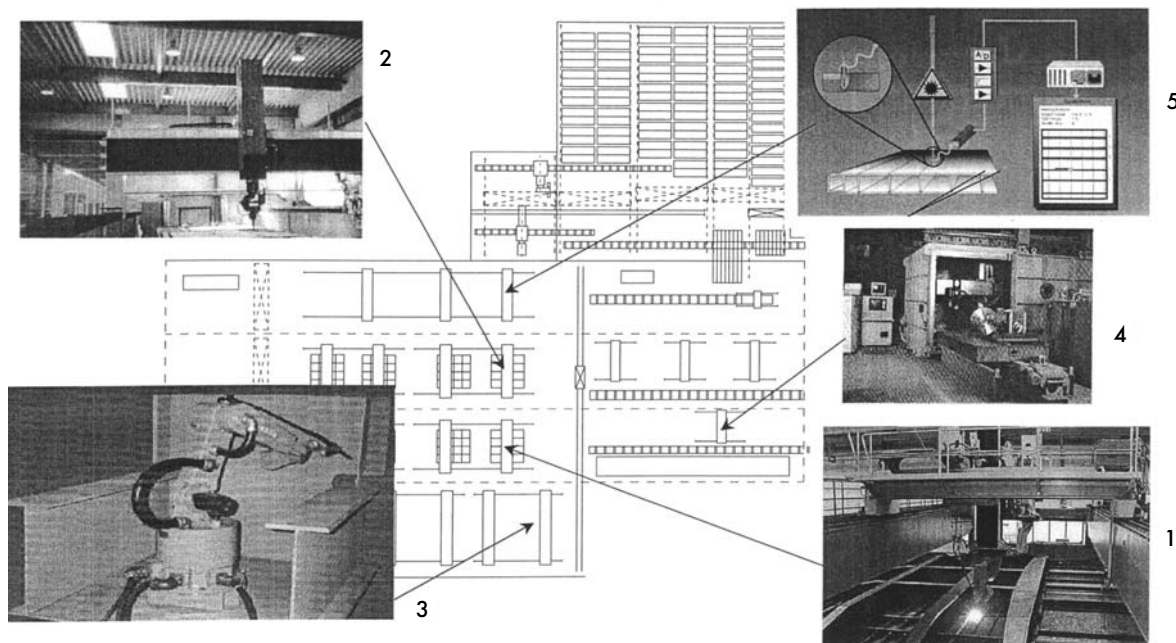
Роботизированные и автоматизированные центры сборочно-сварочного производства:
